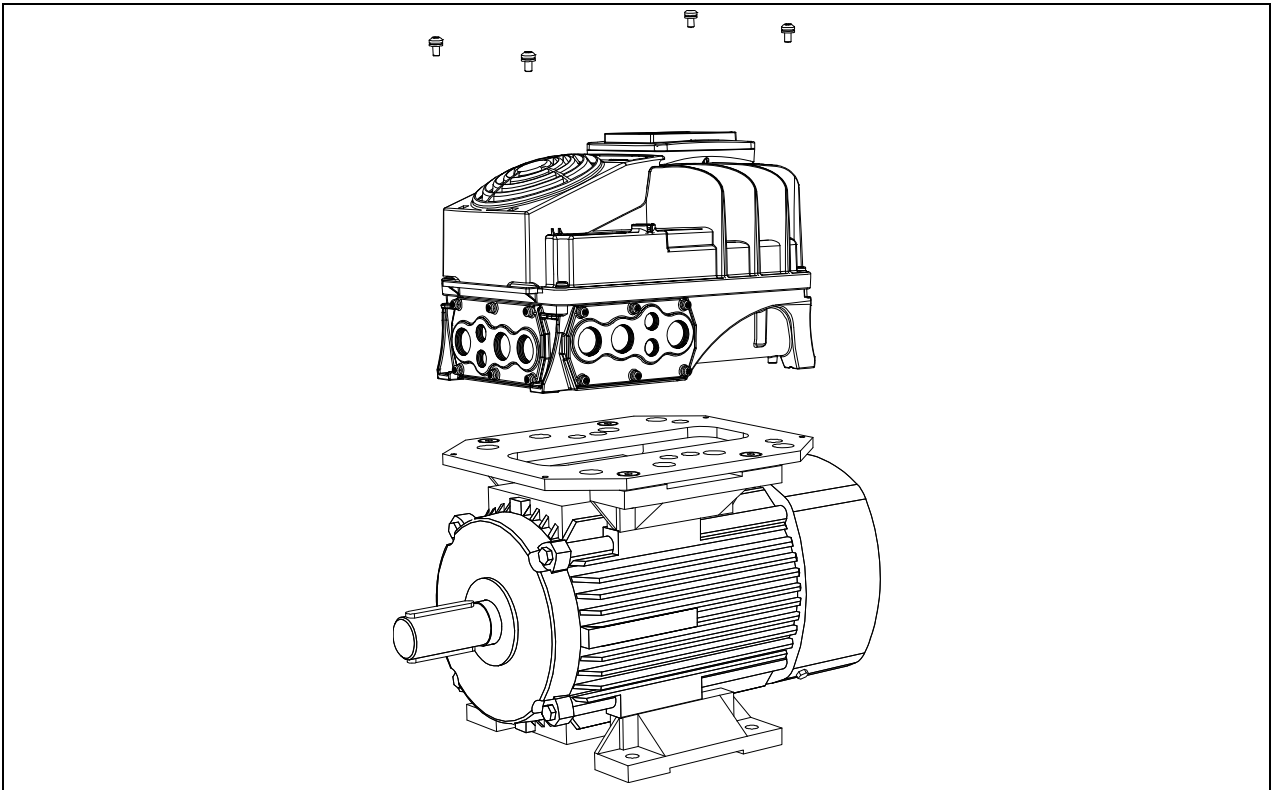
Montieren Sie den Frequenzumrichter mit vier Schrauben auf dem Flanschadapter an.
